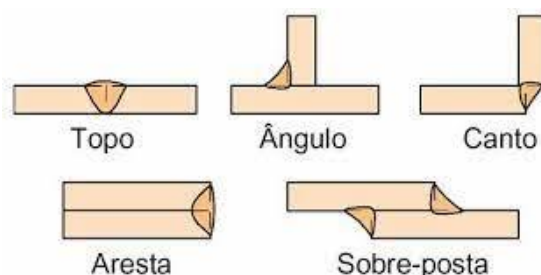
Alguns tipos de junta para soldagem com eletrodo revestido
